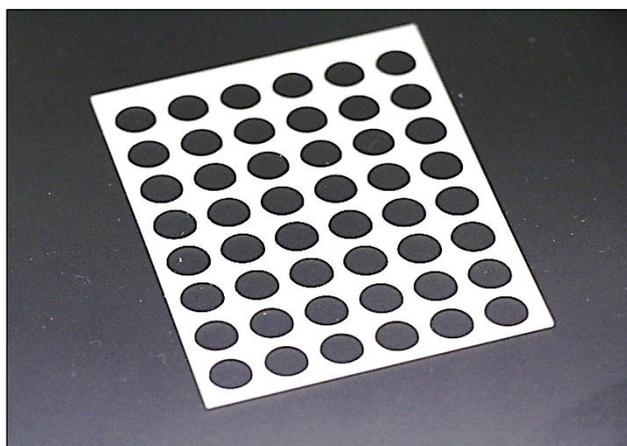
Отверстия, изготовленные в пластине из корундовой керамики методом лазерной фрезеровки
